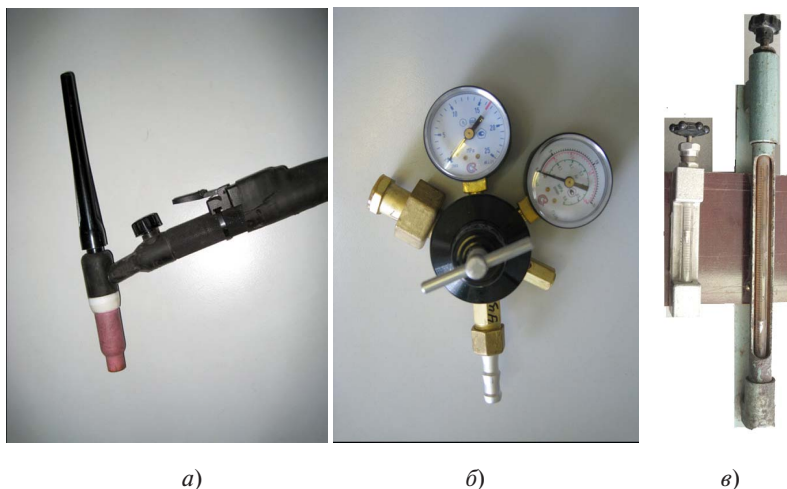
Аппаратура поста для АРДС: а) малогабаритная горелка для сварки неплавящимся электродом; б) редуктор типа ДЗР; в) ротаметры
